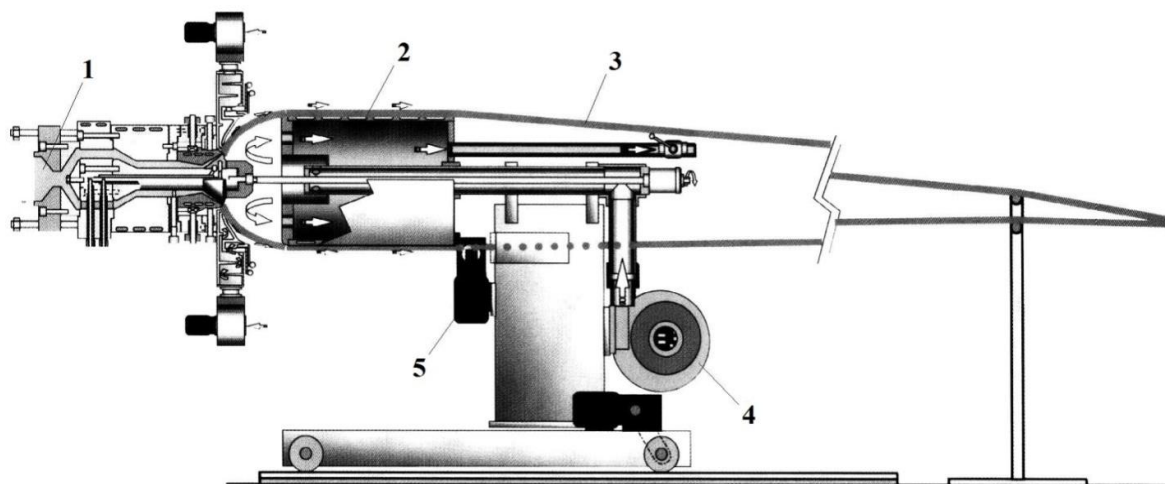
Схема раздувной головки для пленки [4]: 1 – головка; 2 – мандрель; 3 – рукав; 4 – вентилятор охлаждения; 5 – нож
